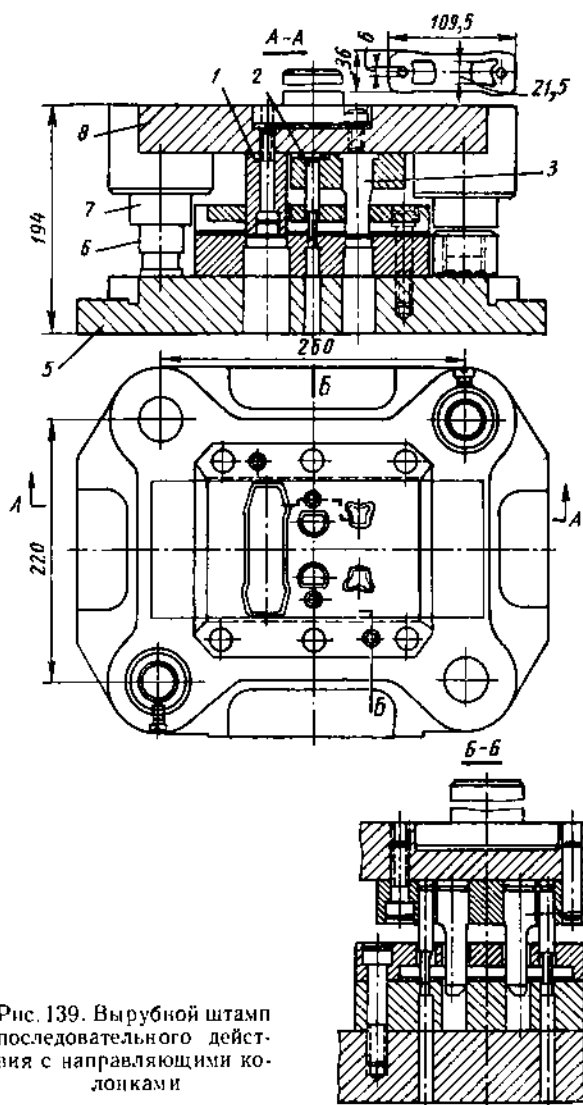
Вырубной штамп последовательного действия с направляющими колонками
